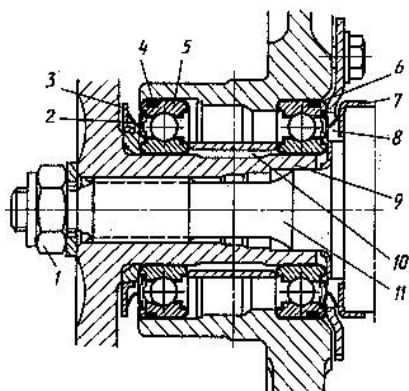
Опора переднего колеса легкового автомобиля с двумя радиальными шариковыми подшипниками 5, оснащенными уплотнителями; справа — фиксированный подшипник, слева — плавающий. Уплотнения, разработанные фирмой СНР, удерживаются наружными кольцами подшипников и скользят как по внутренним кольцам, так и по угловым кольцам 3 и 7, напрессованным на буртики вала. Полости 2 и 8 под боковыми уплотнительными кромками заполнены смазочным материалом. Проникновение воды в полость ступицы предотвращается кольцами круглого сечения 4 и 6, размещенными в канавке наружных колец. При затягивании гайки 1 внутренние кольца зажимаются через дистанционную втулку 10. Вследствие этого вал 11 колеса нагружается на растяжение и кручение; основную часть изгибающих моментов воспринимает шейка 9 ступицы
